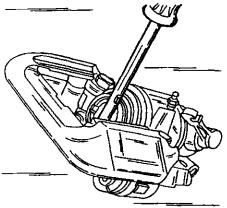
Выворачивание или вворачивание поршня тормозного суппорта заднего колеса.
